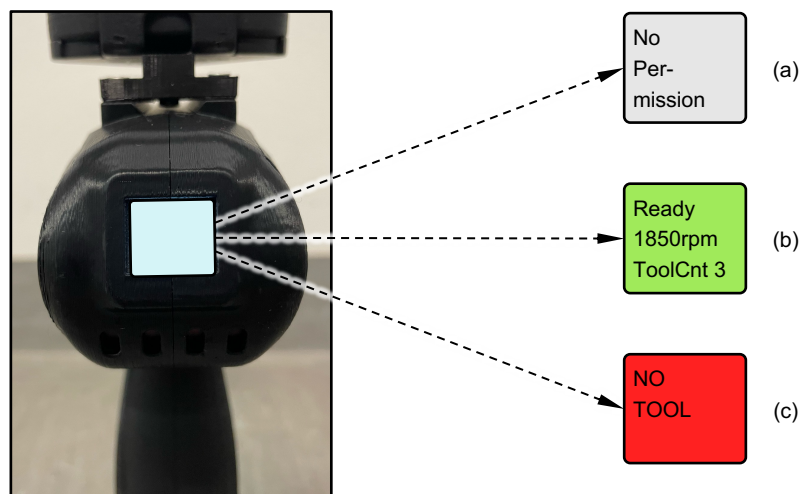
Bildschirmzustände am Smarten Handwerkzeug
